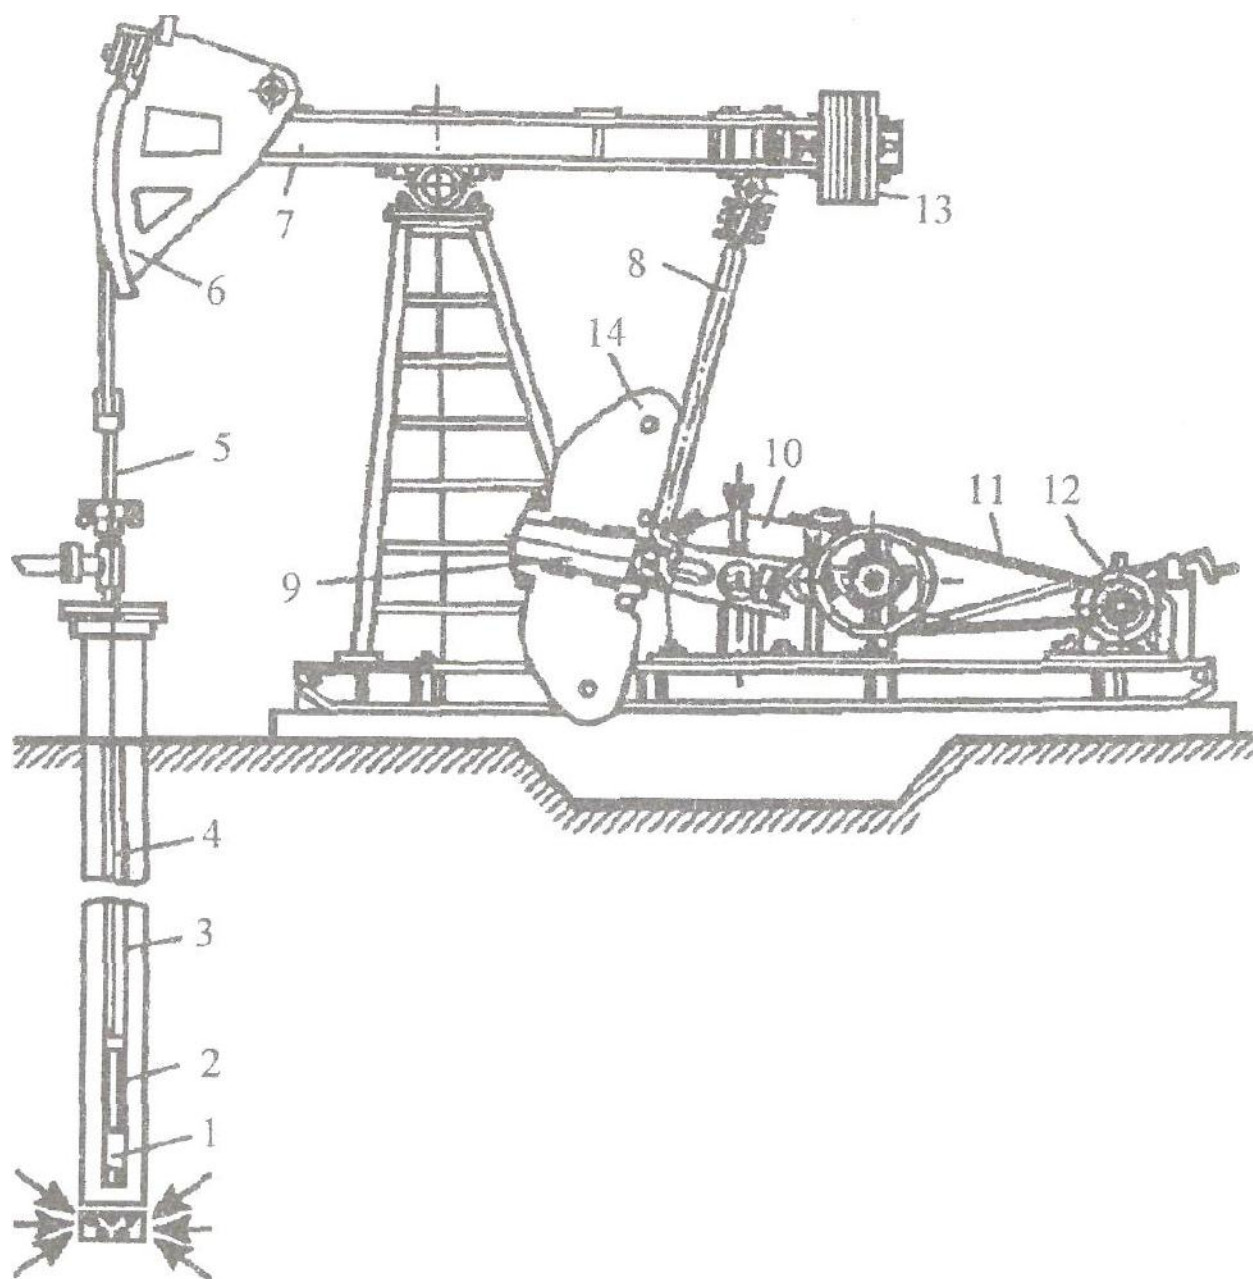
Схема глубинно-насосной установки 1 - плунжерный глубинный насос; 2 - плунжер; 3 - насосные трубы; 4 - штанга; 5 - полированный шток; 6 - головка балансира; 7 - балансир; 8 - шатун; 9 - кривошипный противовес; 10 - редуктор; 11 - клиноременная передача; 12 — электродвигатель; 13 — балансирный противовес; 14 - кривошипный противовес
